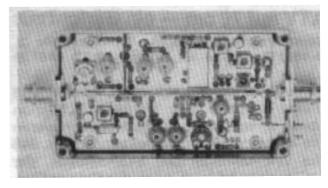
Musteraufbau SSB-Ausführung, Platine in Gehäuse eingebaut
